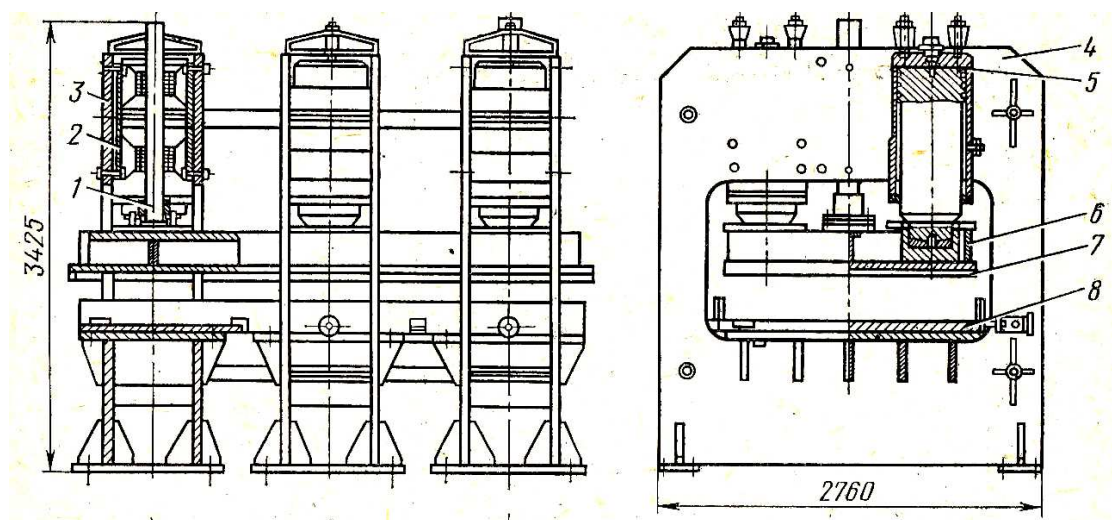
Одноэтажный пресс ПР-5 (М) для подпрессовки пакетов:
